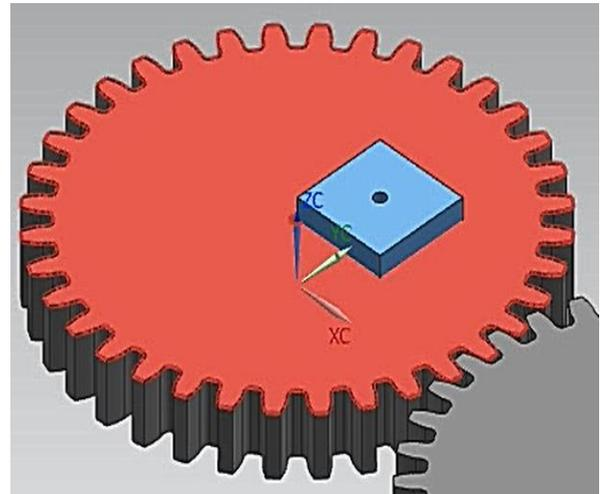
Cara superior de pieza engrane1.prt.
